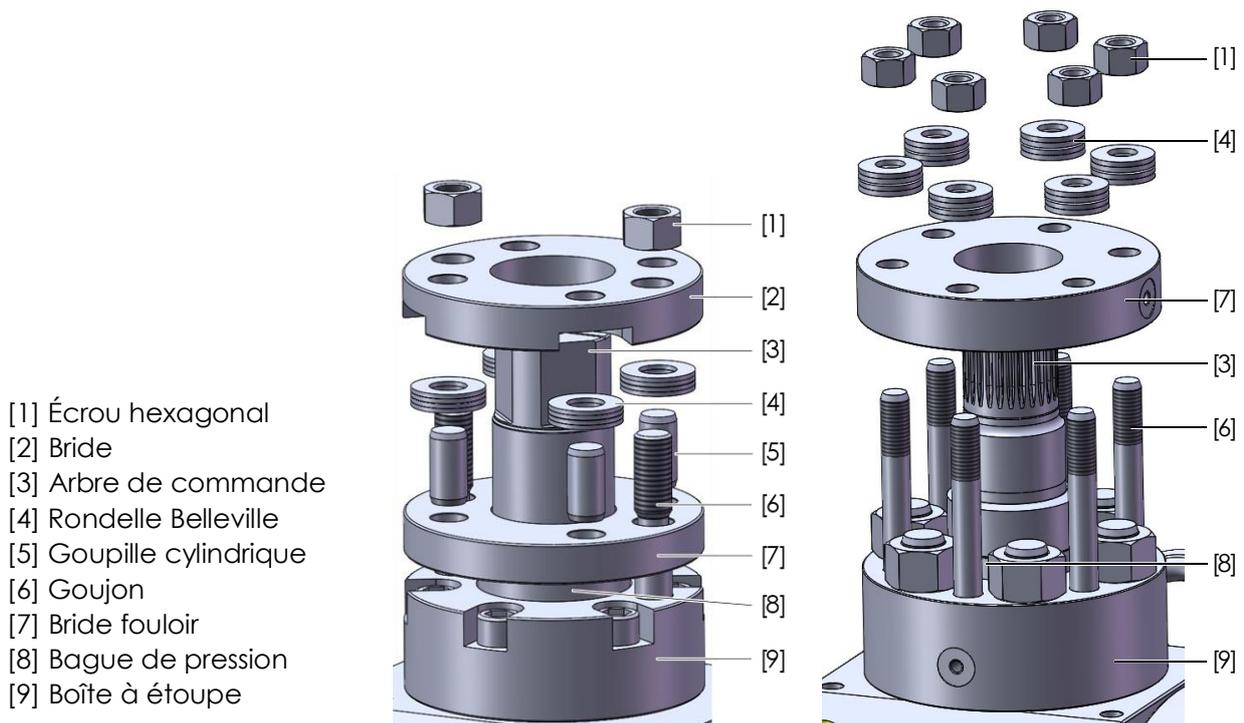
Variantes du presse étoupe équipé d'une garniture de presse étoupe live loading (démontée)
